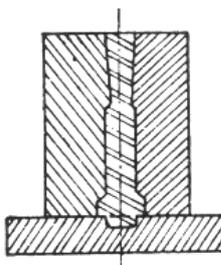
Coquilla formada por dos placas y pedestal.
